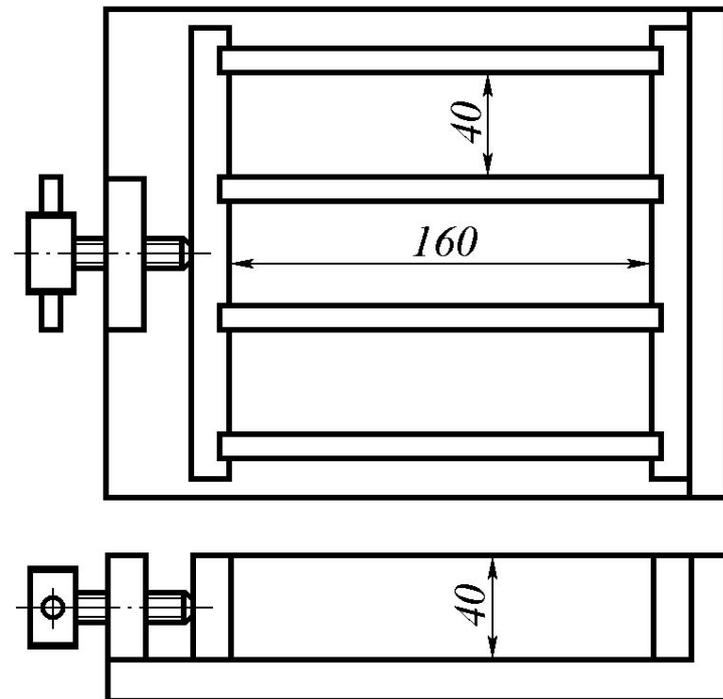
Разборная форма для изготовления образцов-балочек
